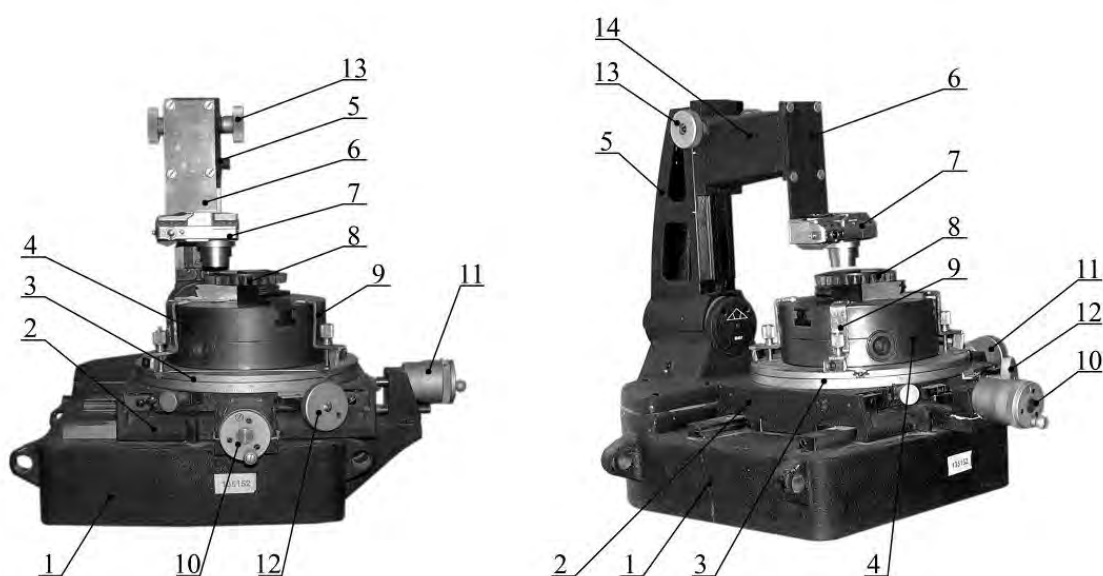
Устройство для контроля сложнопрофильных поверхностей деталей ППП
